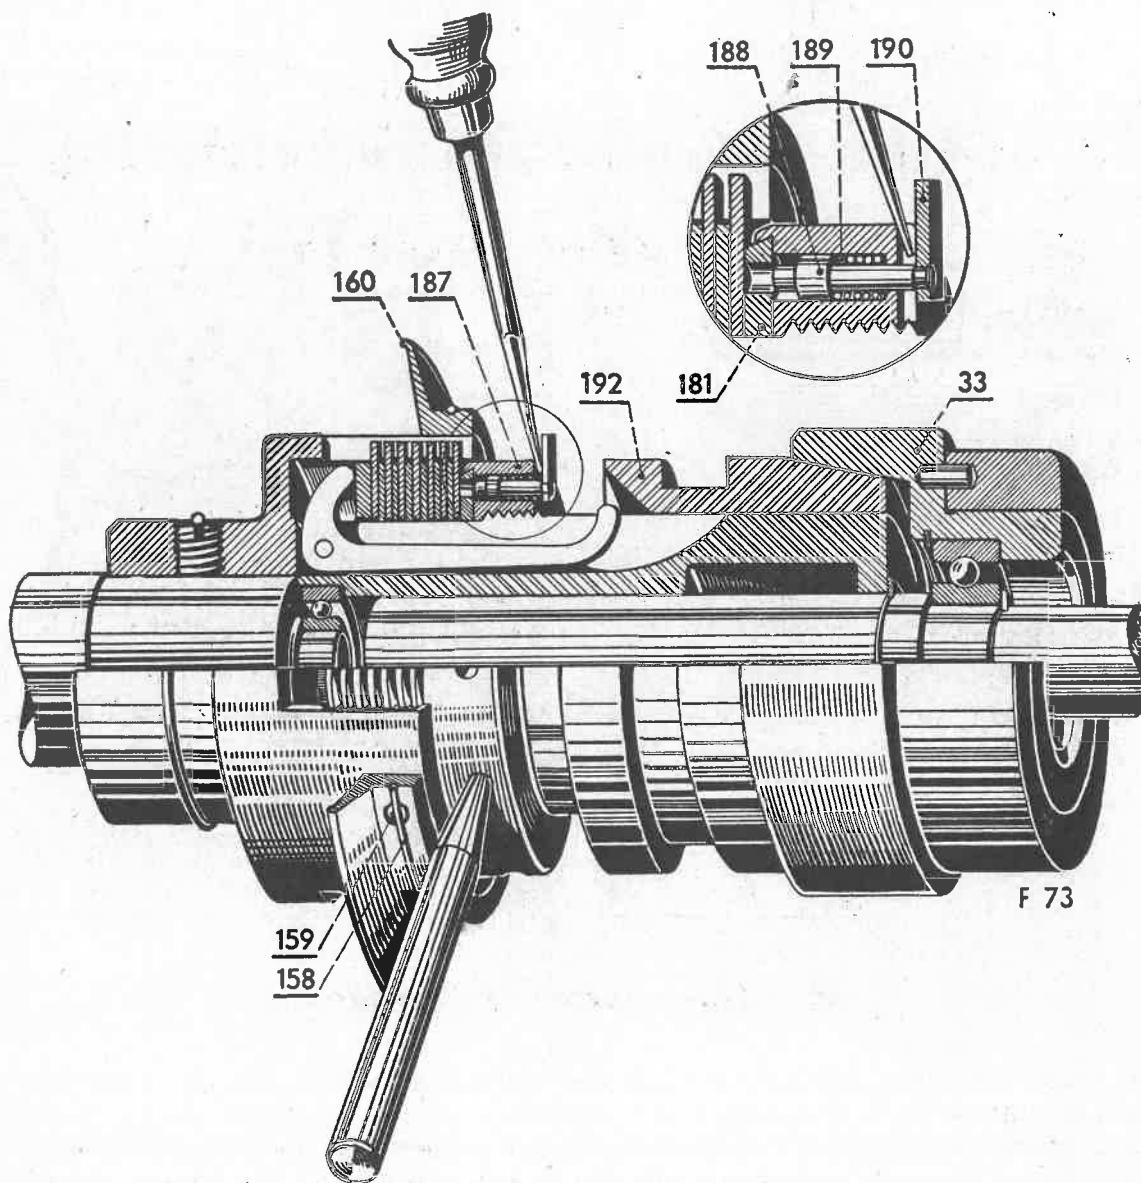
Seřízení ložisek vřetena stroje FV 1.
